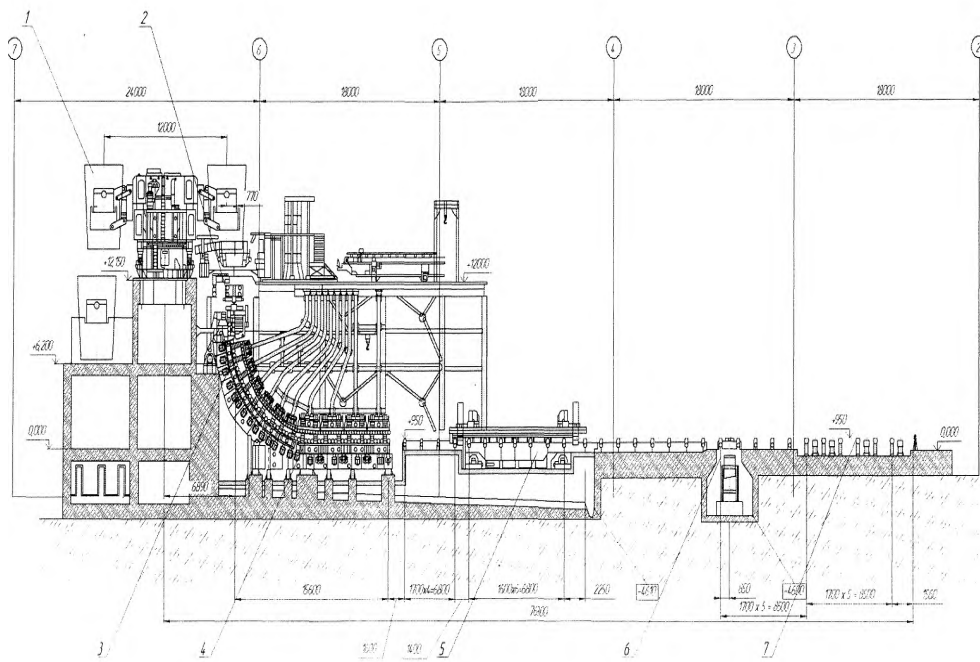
Машина безперерного лиття заготовок криволінійного типу
